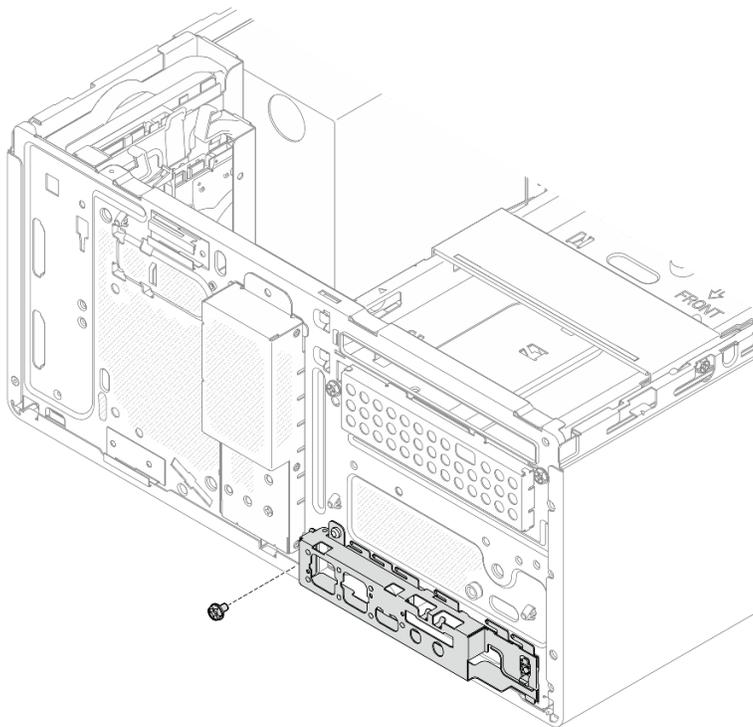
Removendo o parafuso que fixa o suporte de E/S frontal
